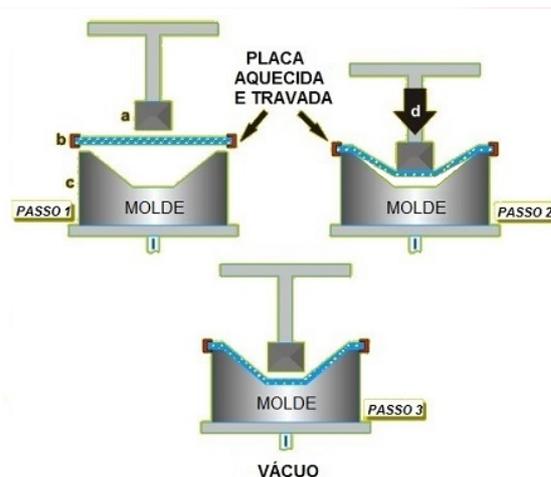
Moldagem com plug ou contramolde auxiliar (Fonte: Tudo sobre Plásticos, 2014).
